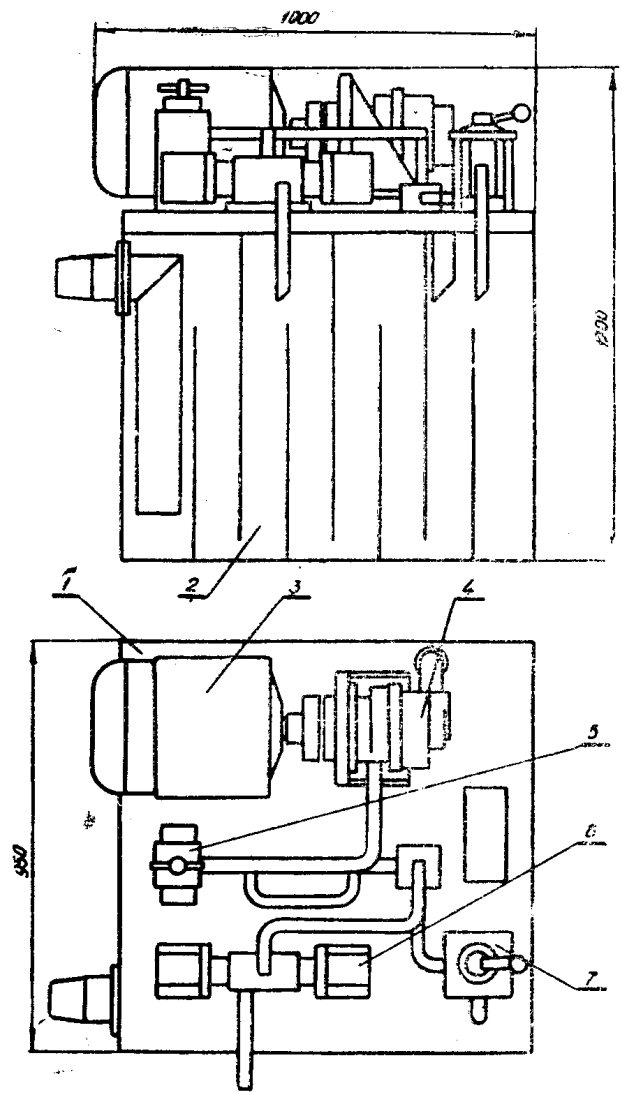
Общий вид высоконапорной установки для подачи СОЖ
